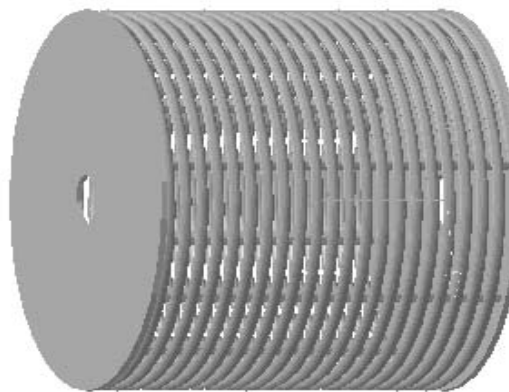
Циліндричний барабан із прутковою поверхнею
